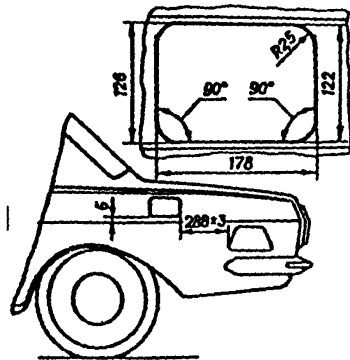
Разметка отверстий на правой распорке щитка передка для крепления газового фильтра
